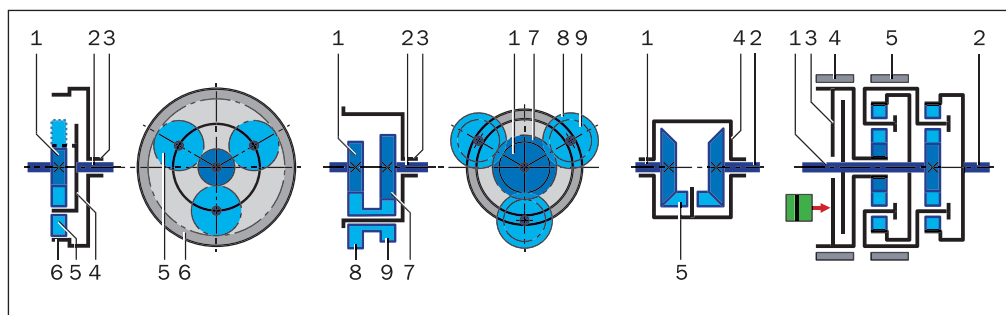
Варианты исполнения планетарных передач: 1, 2, 3 — валы; 4 — водило; 5, 8, 9 — сателлиты; 6, 7 — коронное зубчатое колесо
